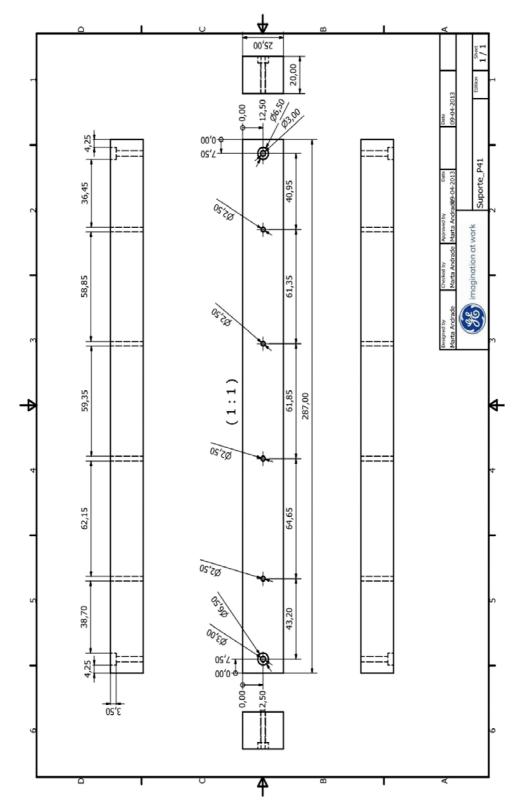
Desenho técnico do suporte dos blocos padrão da PMAU 41
